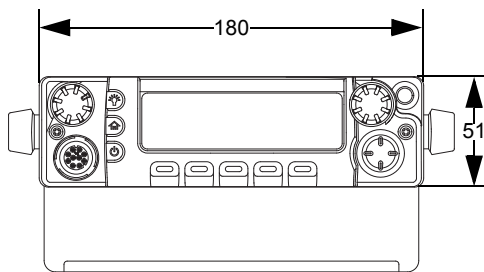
Vista Frontal da Cabeça de Controle O5 com Munhão e Montagem Remota
